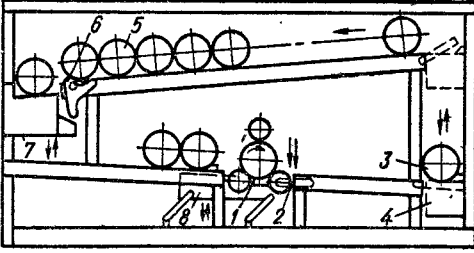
Схема вертикально-замкнутой поточной линии для центробежной отливки труб:
